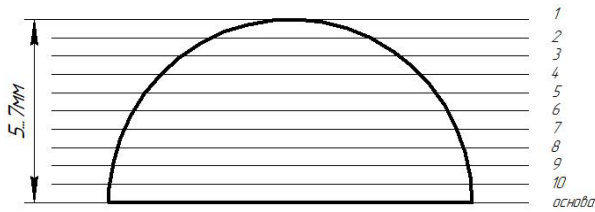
Схема послойного снятия металла сварочной точки
